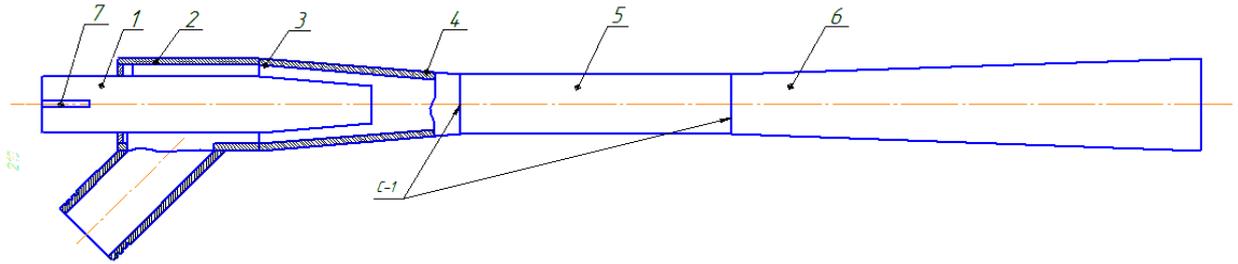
Ежектор: 1 – сопло; 2 – фланець; 3 – кожух; 4 – корпус; 5 – труба; 6 – раструб; 7 – патрубок.
